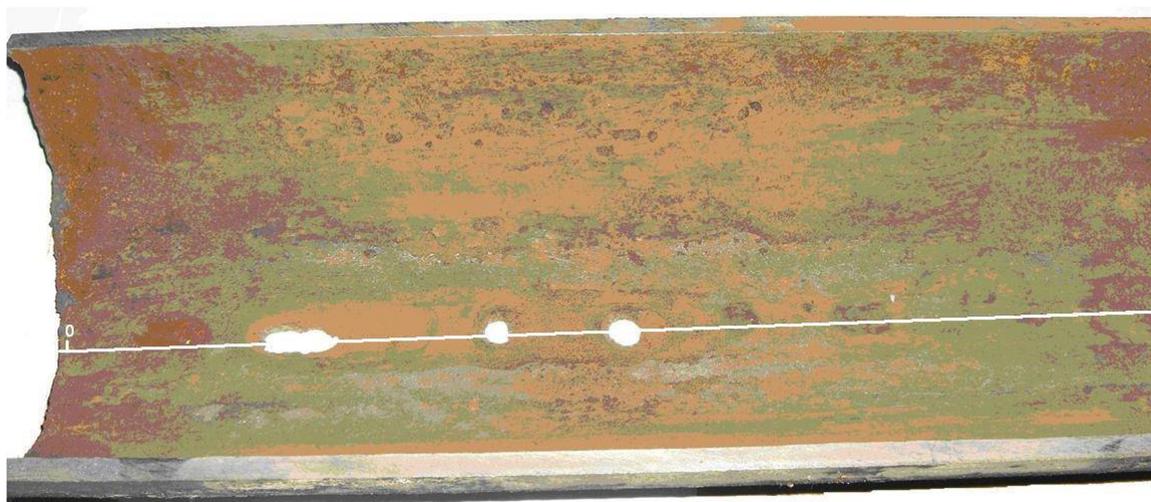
Вид образца трубы со сквозными коррозионными дефектами
